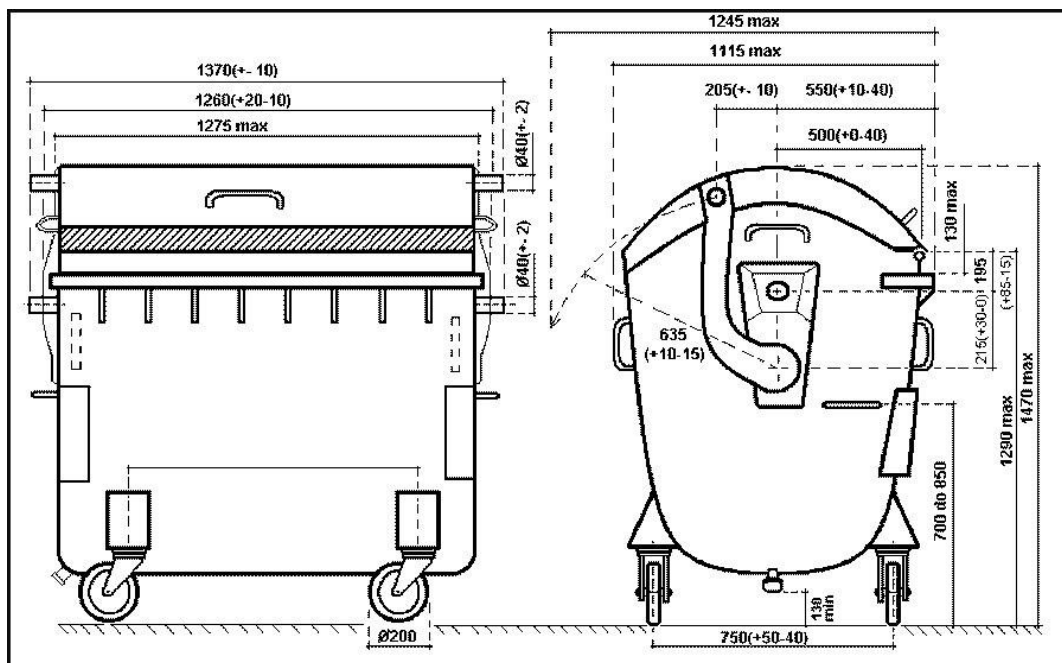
Оцинкованный контейнер 1,1 м³, предназначенный для сбора ТБО.
